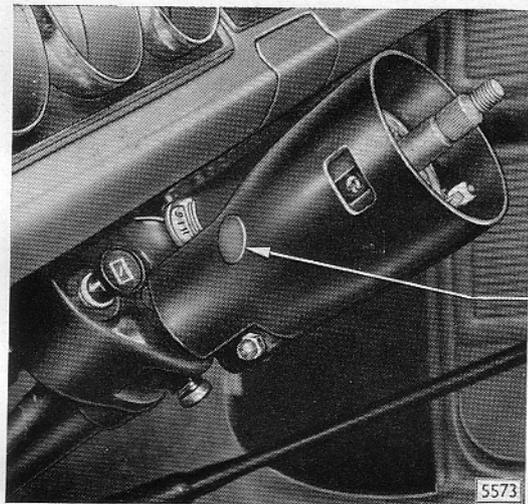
Unter jeweiligem Gummiverschlußdeckel links wie rechts liegt obere Gehäusebefestigungsschraube (insgesamt 2 Stück)
